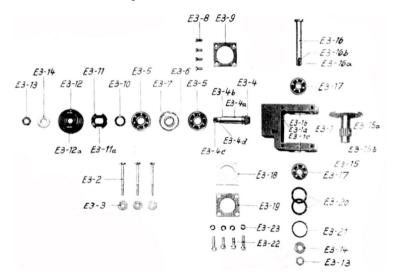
ED 151 B; Zahnradgetriebe; Einzelteile
